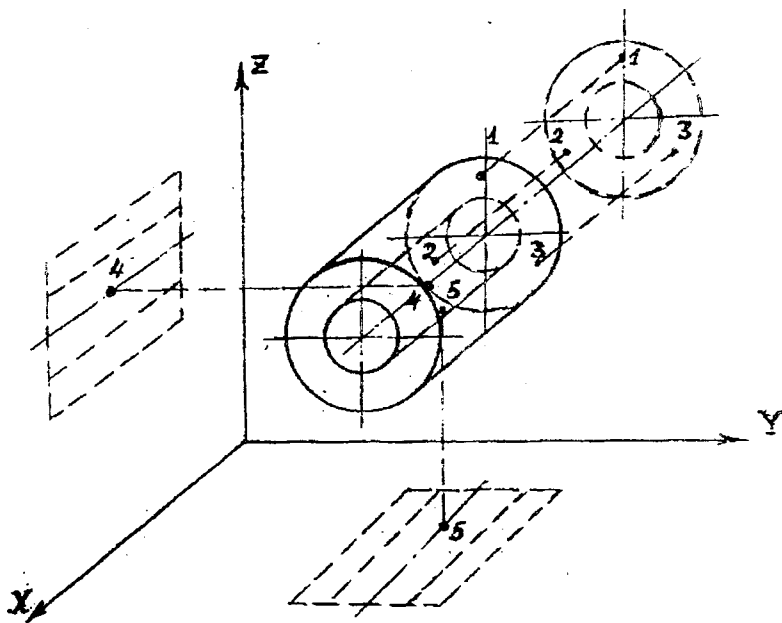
Схема базирования заготовки по цилиндрическому отверстию
